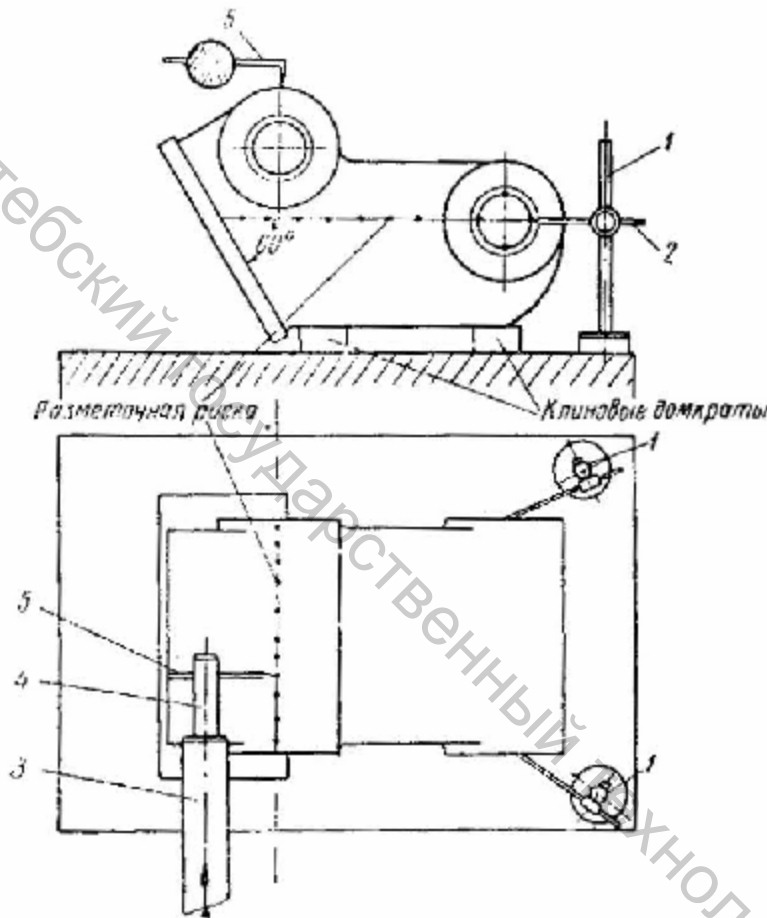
Проверка положения детали относительно станка по разметочным рискам
